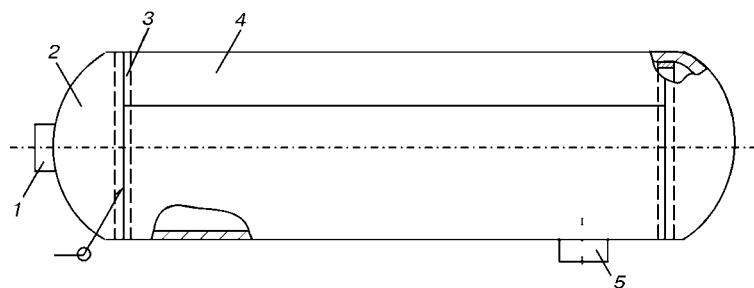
Схема разделения резервуара на конструктивные элементы: 1, 5 — штуцера; 2 — днище; 3 — кольцо подкладное; 4 — обечайка
